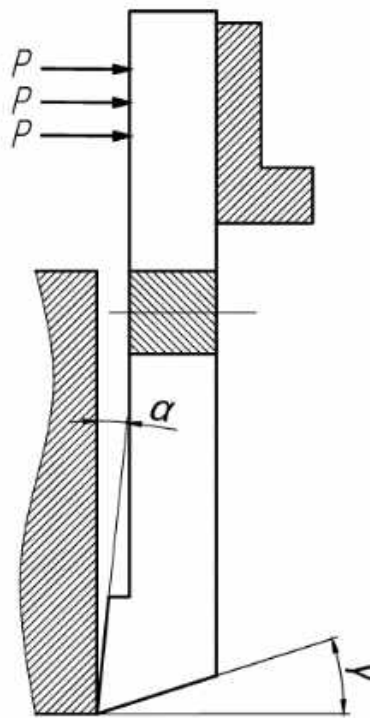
Схема обробки поверхні довбальним різцем
